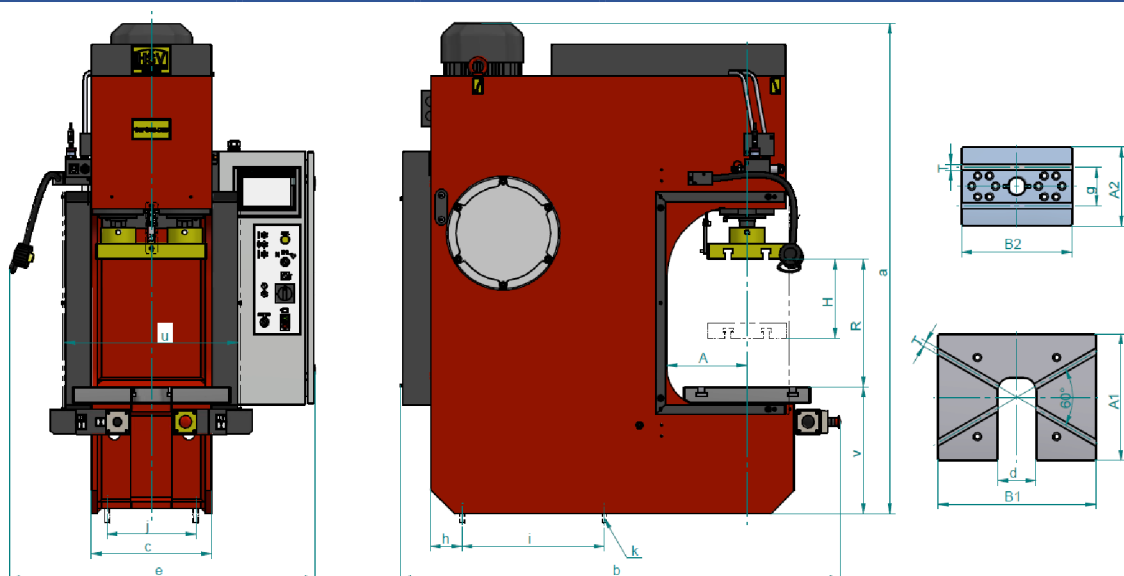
Hydraulický lis CUPS 16 DEU [36].
